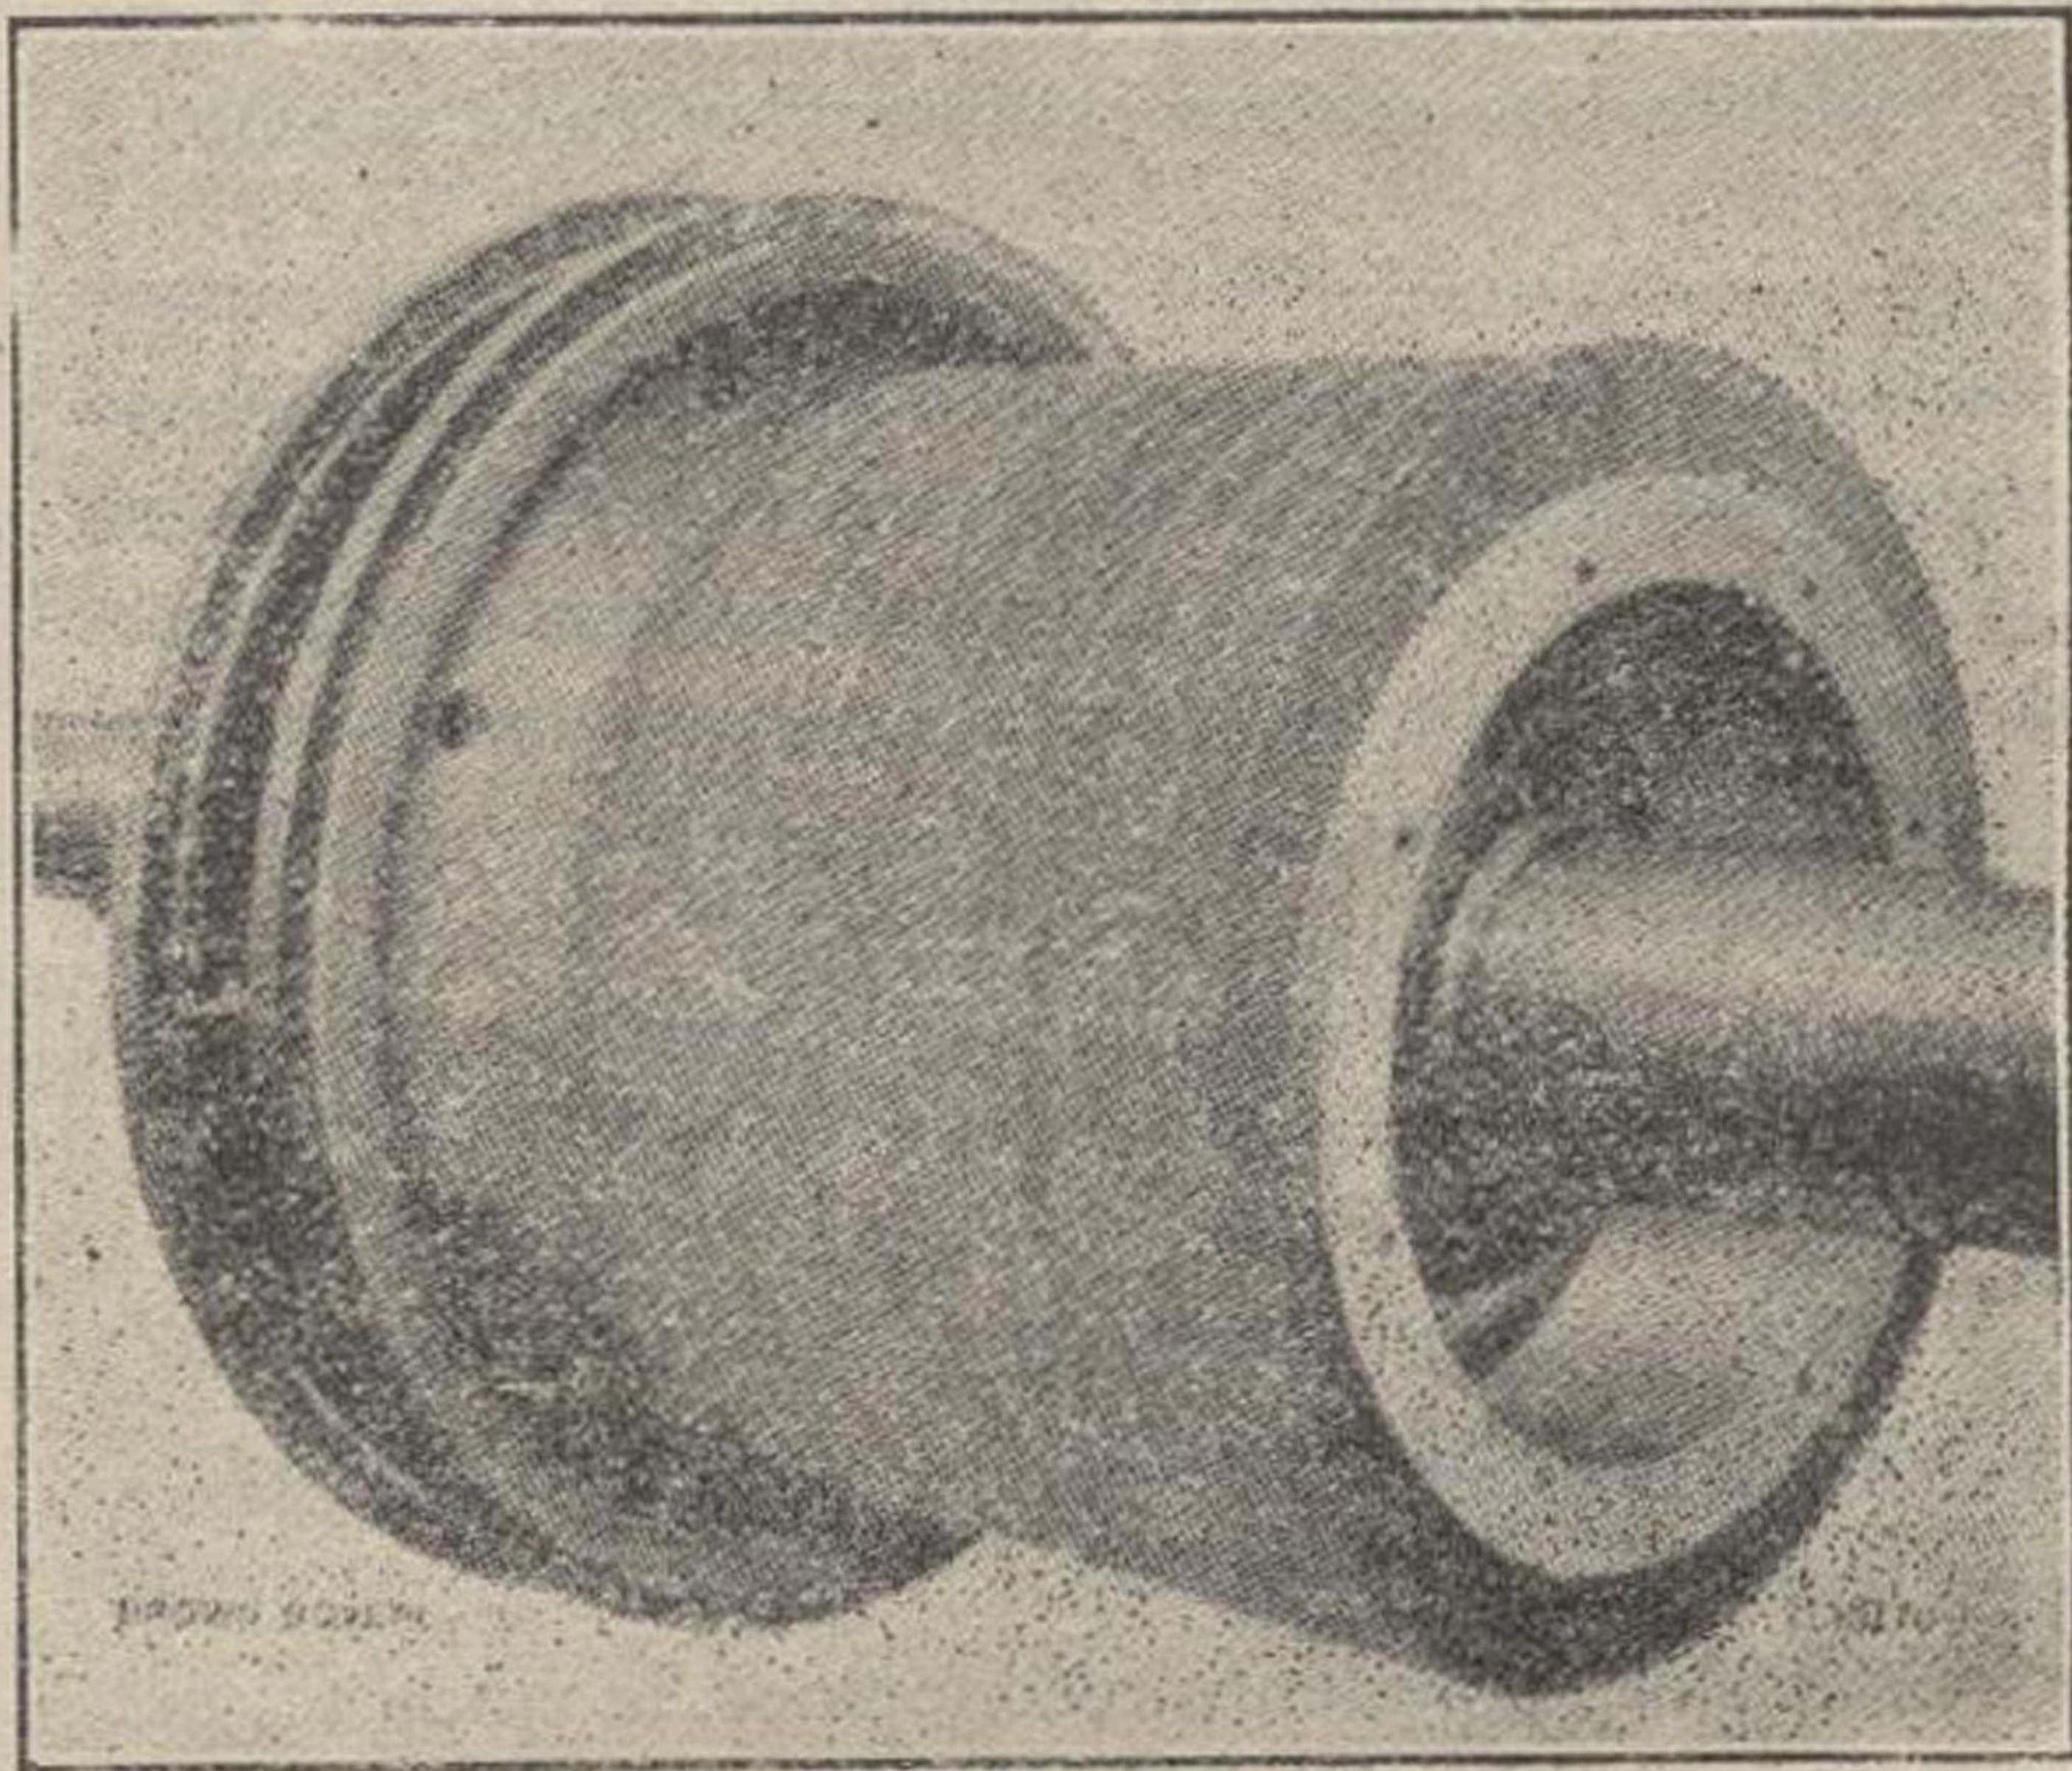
Rotor de la parte alta presión de una turbina de tres cilindros de 15.000-20.000 kilovatios, 3.000 revoluciones por minuto.
